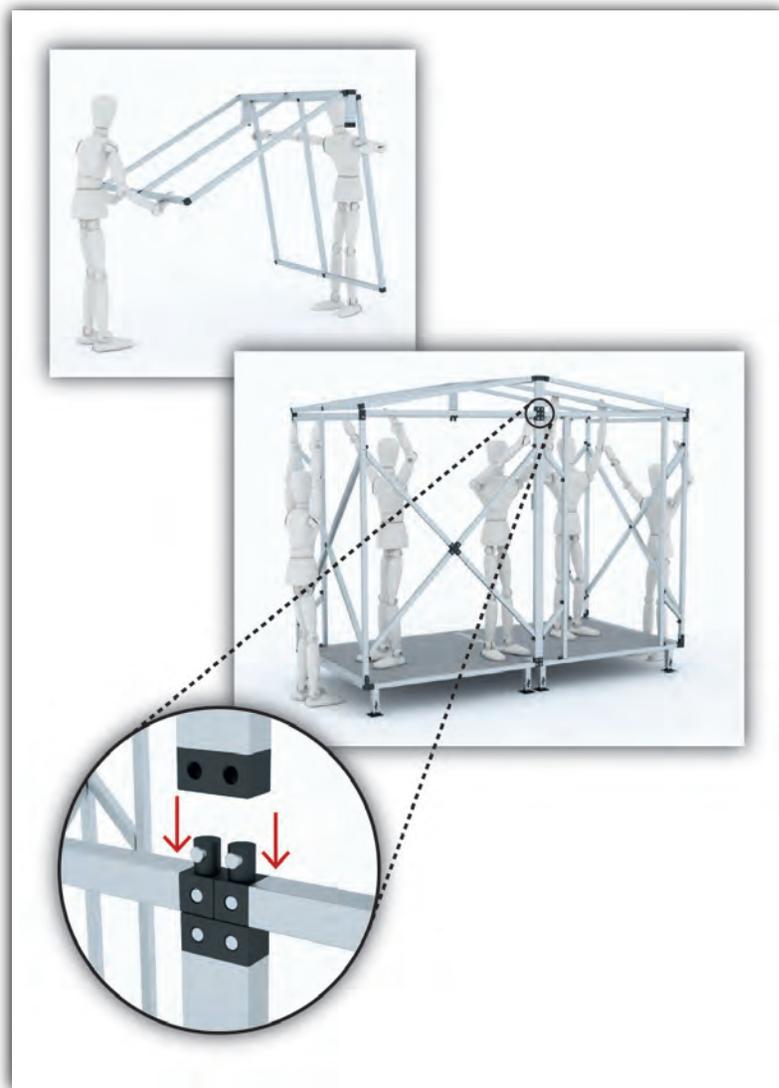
Apertura de conjunto techo y colocación del mismo sobre la estructura base, y ensamble con largueros y columna central.
